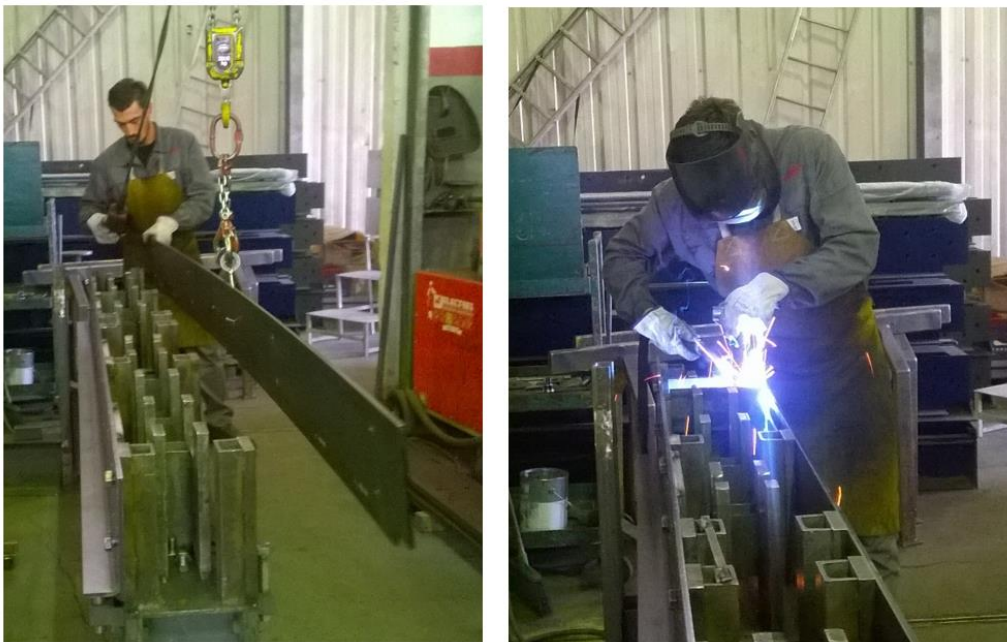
Po. 3 – Posto de soldadura de módulo para báscula
